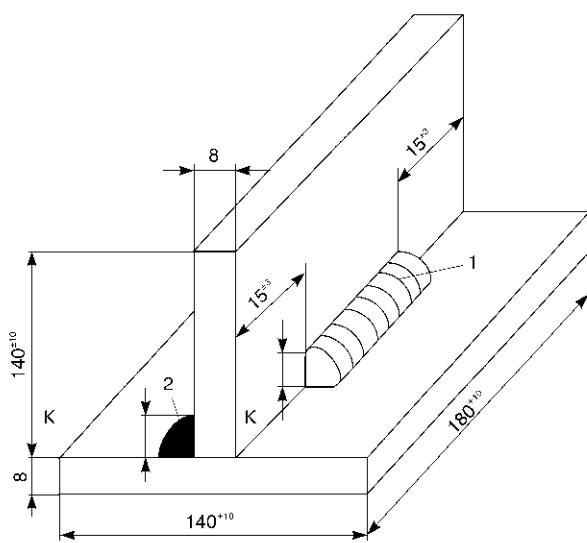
Тавровый образец для проверки сварочно-технологических свойств: 1 — контрольный сварной шов; 2 — сварной шов, обеспечивающий жесткость образца (выполняется только на двустороннем тавровом образце)
